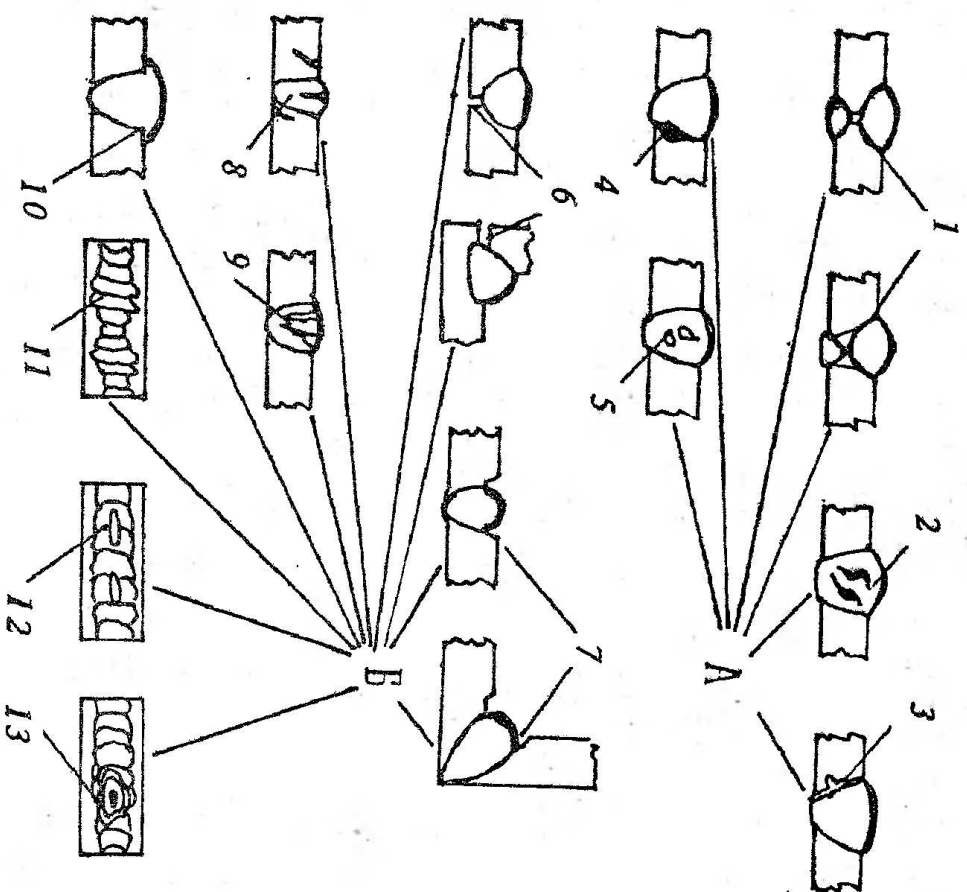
Внутренние (А) и наружные (Б) дефекты сварных швов. 1 — непровар; 2 — трещины; 3 — несплавления; 4 — поры; 5 — непровар; 6 — подрезы; 7 — трещины; 8 — поры; 9 — наплывы; 10 — шлак; 11 — трещины; 12 — прожоги; 13 — кратер
